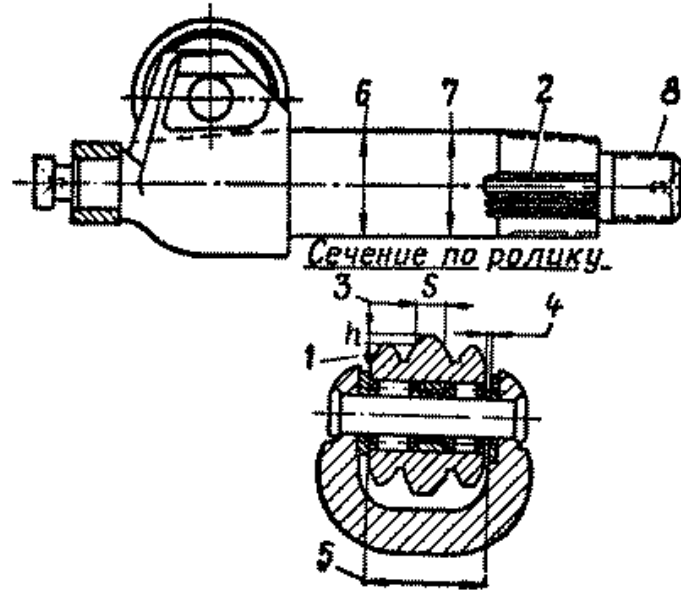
Вал сошки рулевого управления с роликом в сборе
